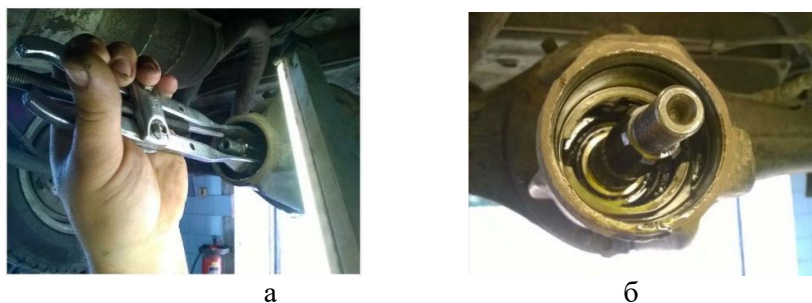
Знімання зовнішньої обойми підшипника (а); Редуктор без підшипника (б)
